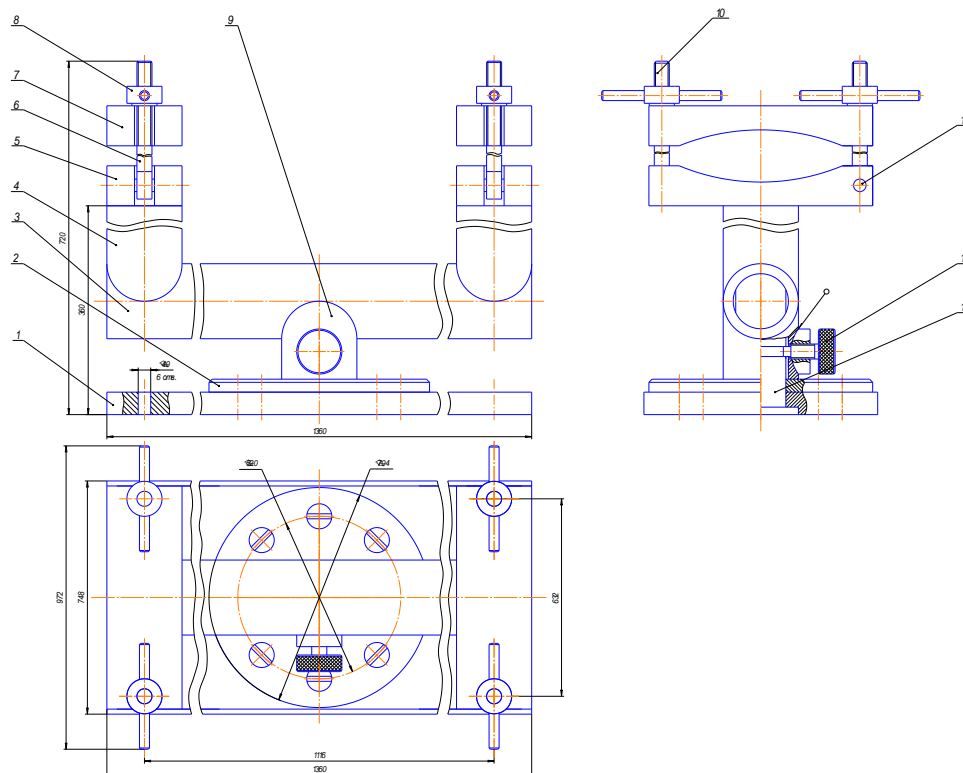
Приспособление для разборки и сборки ведущих мостов автомобилей.
